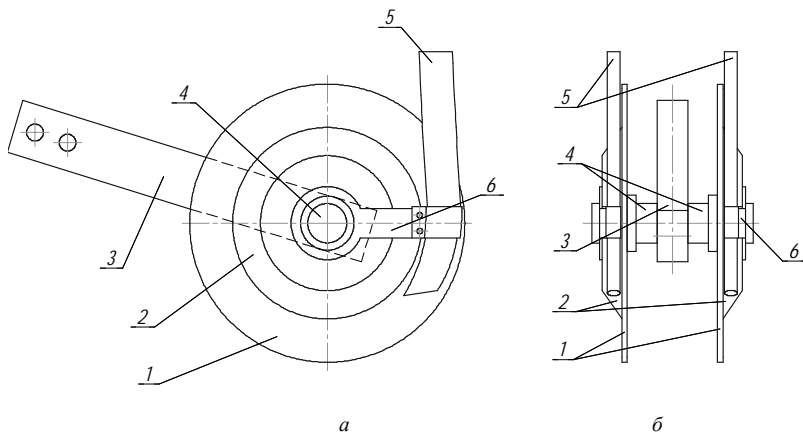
Комбинированный двухдисковый сошник для посева семян зерновых и мелкосеменных культур: *a* – вид сбоку; *б* – вид сзади; 1 – плоский диск; 2 – реборда-бороздкообразователь; 3 – корпус; 4 – ось; 5 – семянаправители; 6 – пластина
